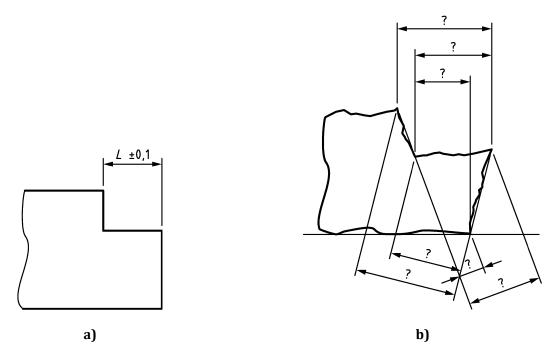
Beispiel für einen linearen Abstand, der zwischen zwei integralen Geometrieelementen verwendet wird, die in der gleichen Richtung ausgerichtet sind
